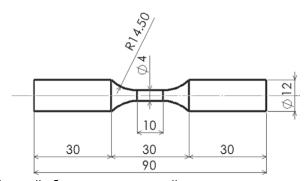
Типовой образец для испытаний на сопротивление усталости [5]
